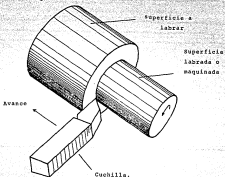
Esquema de los movimientos de trabajo durante el torneado.
